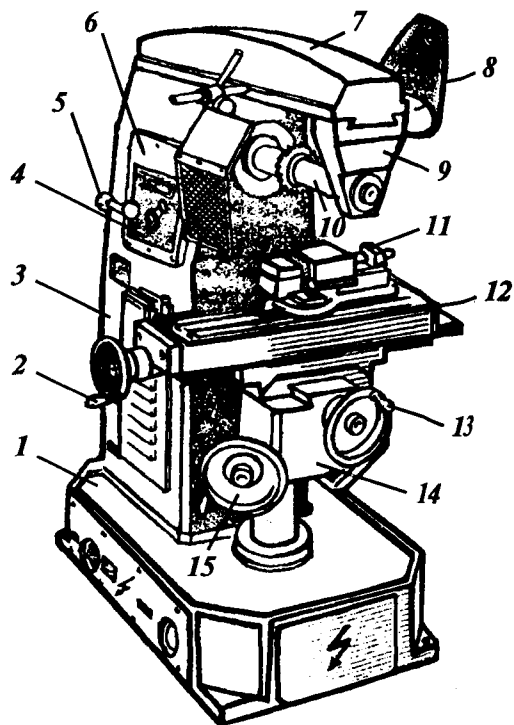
Горизонтально-фрезерный станок НГФ-110Ш:
